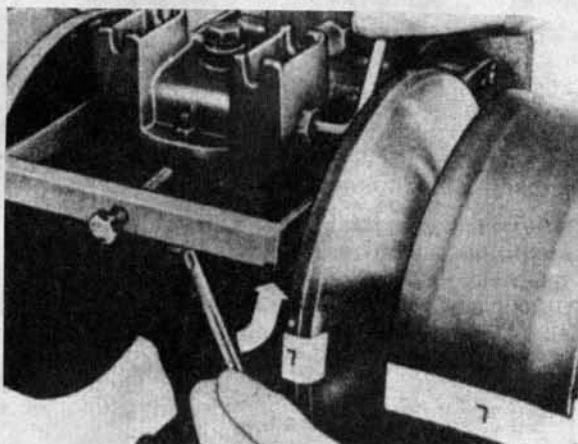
Коробка CVT – регулировка системы блокировки коробки
